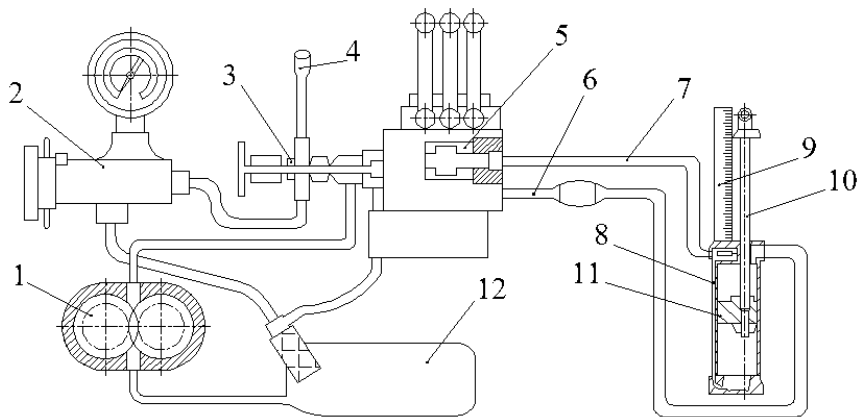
Схема подключения прибора КИ-1097Б и приспособления КИ-6272
